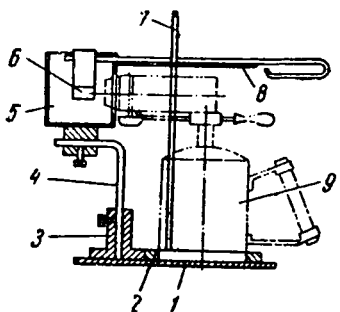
Приспособление для нагрева паяльника паяльной лампой
